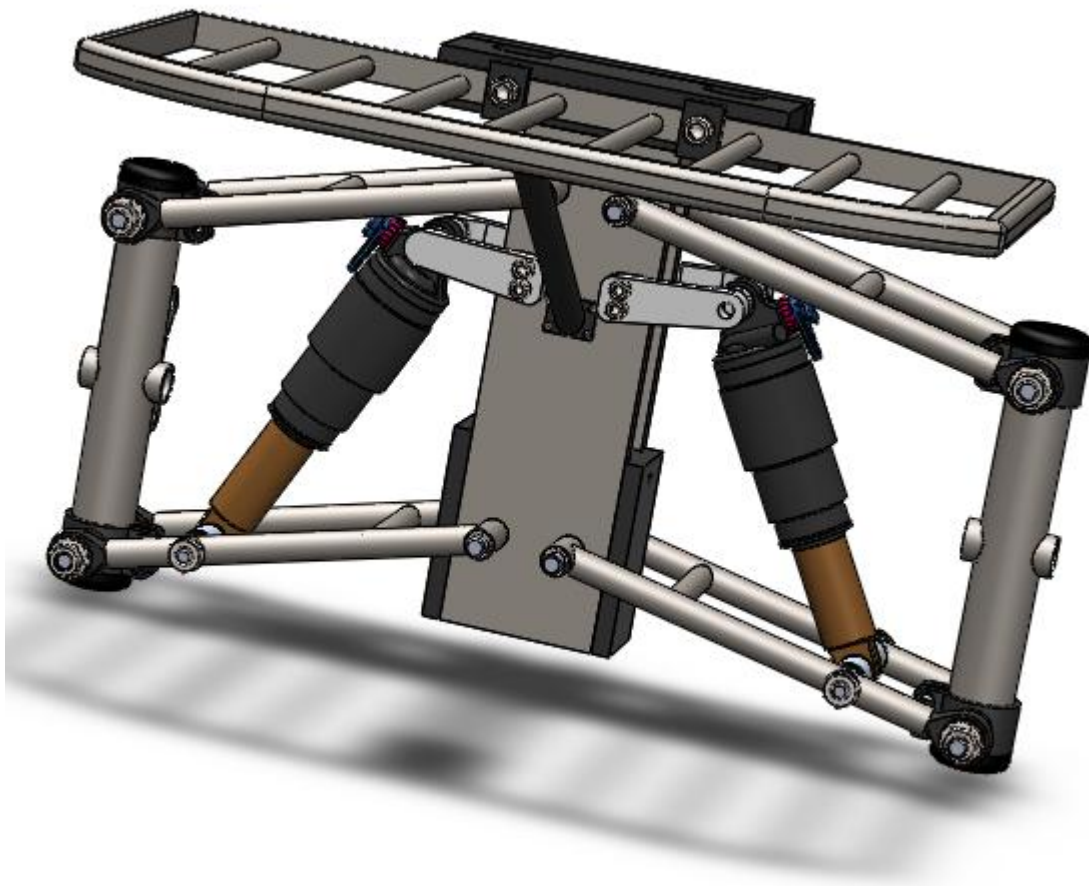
Vue 3D de l'assemblage porte bagage -châssis
